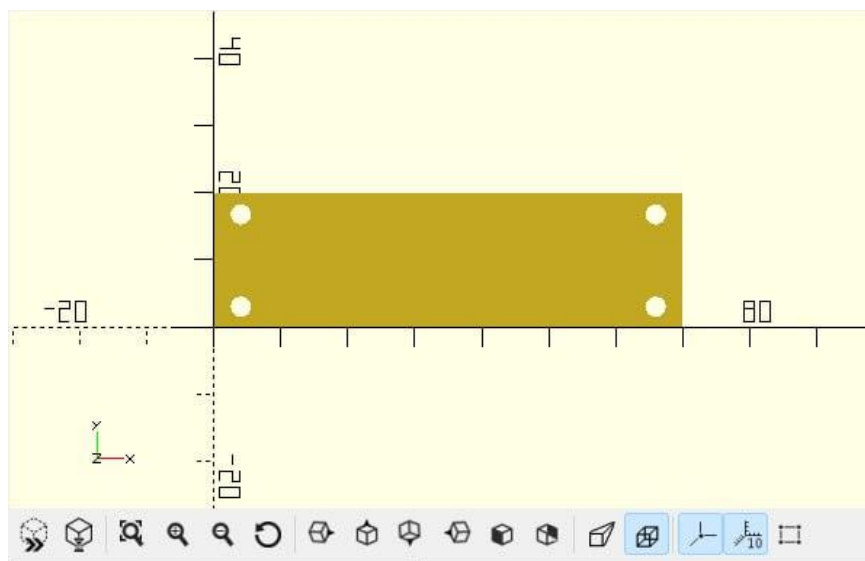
Створена деталь в середовищі OpenSCAD
